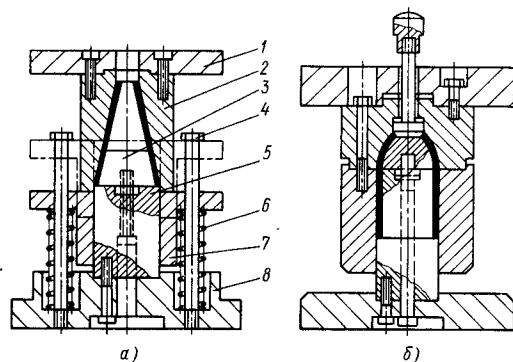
Конструктивные схемы штампов для обжима конусных (а) и куполообразных (б) деталей:
